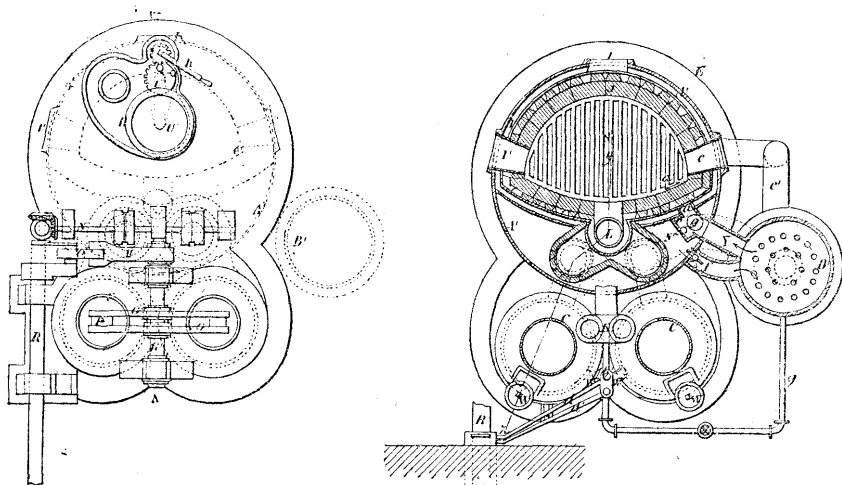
et 139. — Moteur Shaw, plan et coupe horizontale par le foyer.
